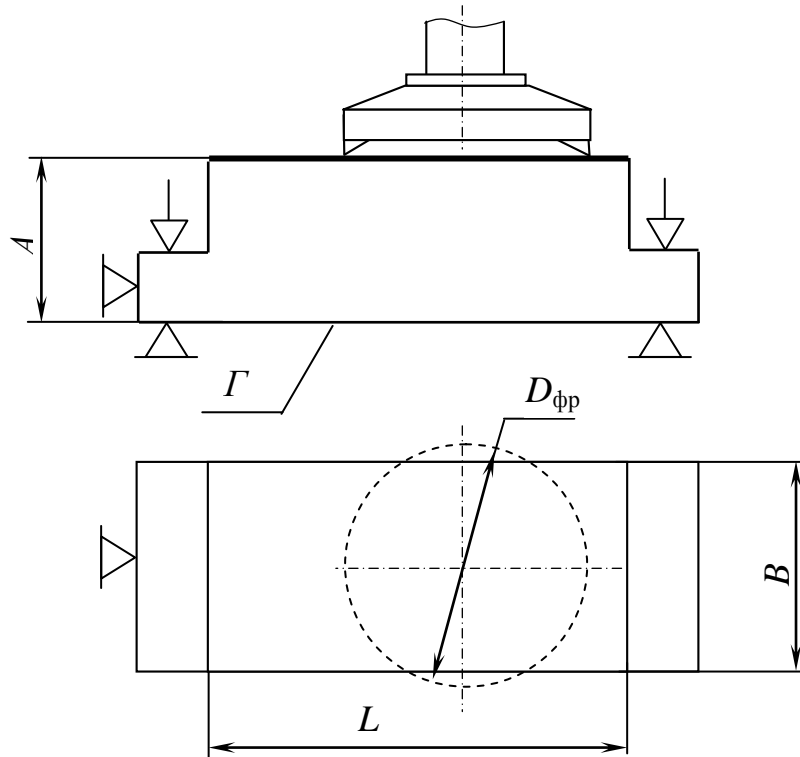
Операційний ескіз до визначення сумарної похибки фрезерної обробки
